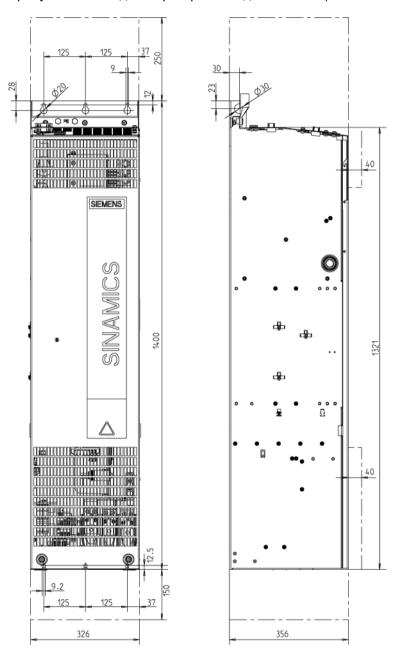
Габаритный чертеж активного модуля питания, типоразмер FX. Вид спереди, вид сбоку
